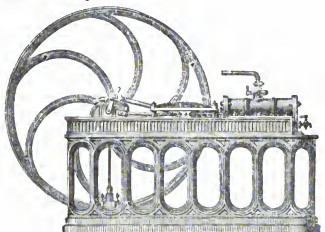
Machine à vapeur fixe de M. Lotz, à Nantes.
